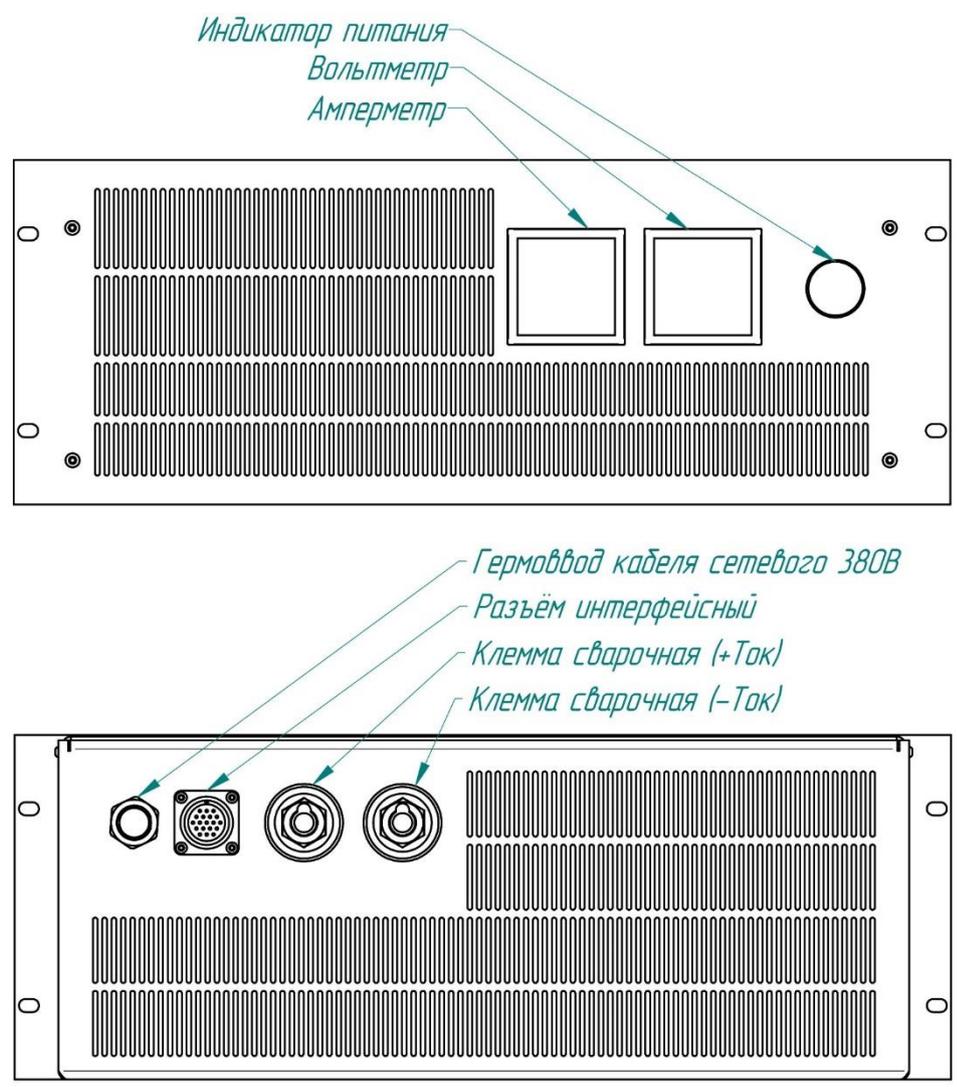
Описание индикаторов и разъёмов источника сварочного DC250
